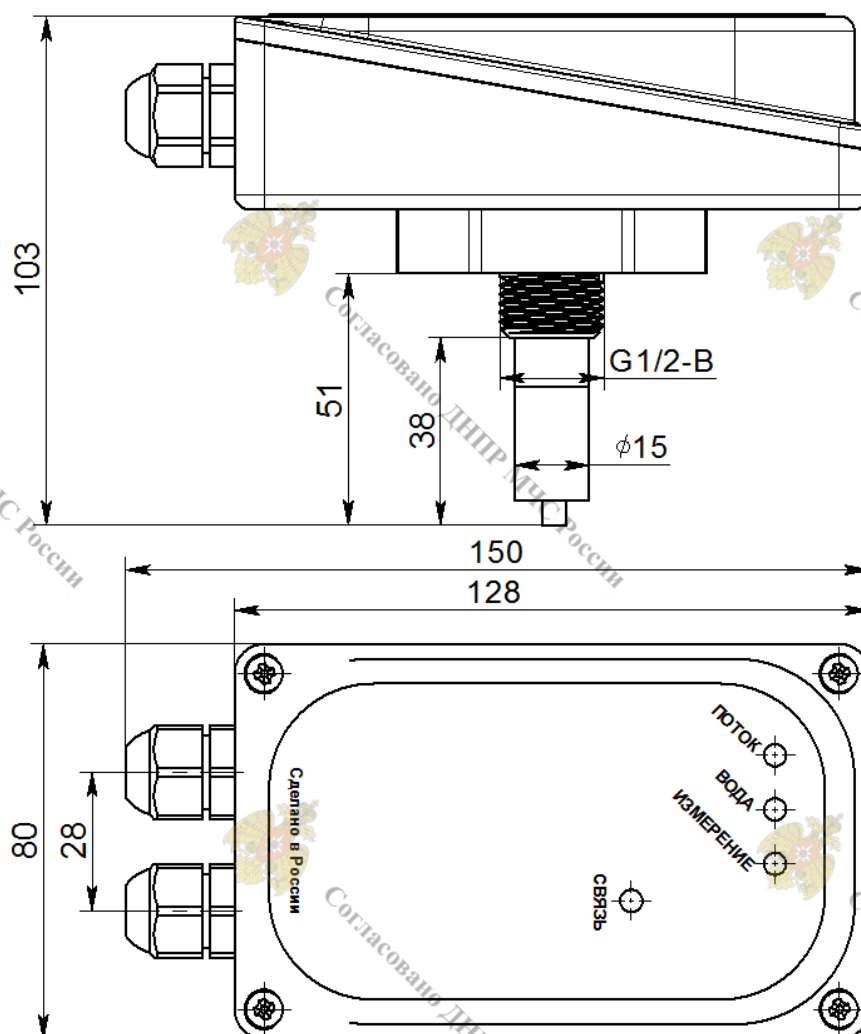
Внешний вид и габаритные размеры СПЖ «Стрим»
